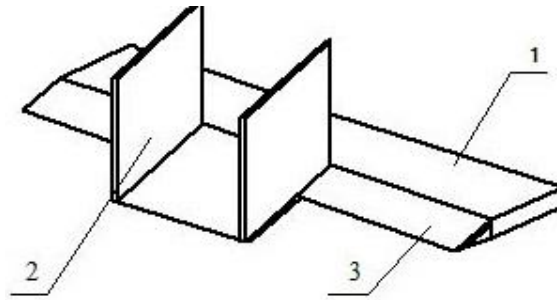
Совковый режущий орган: 1 – днище ковша; 2 – сменный совковый орган; 3 – подножевая плита
